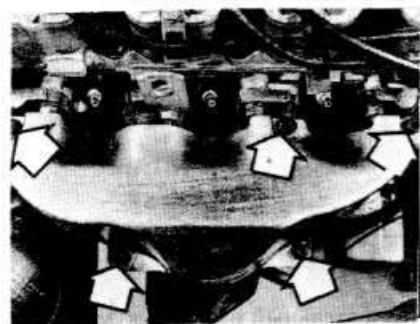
Болты кожуха горячего воздуха впускного коллектора — двигатель 1,6 л с многоточечным впрыском топлива
